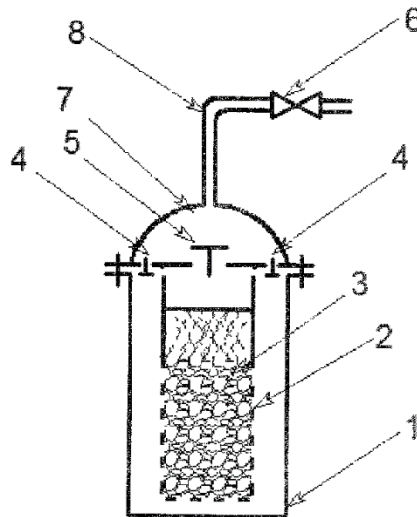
Вариант исполнения порошкового огнетушителя с пористой емкостью: 1 – корпус огнетушителя; 2 – сосуд для хранения порошка; 3 – огнетушащий порошок; 4 и 5 – обратные клапаны; 6 – вентиль; 7 – клапанная коробка; 8 – трубка
